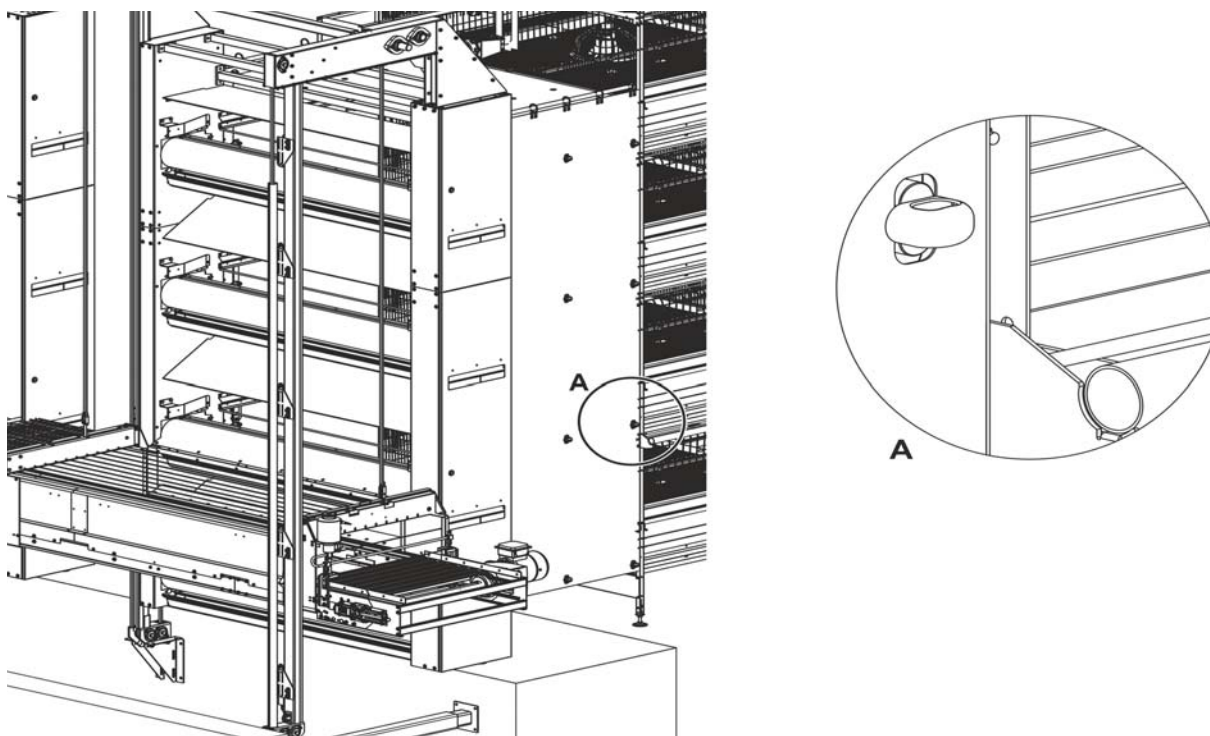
Cortinas de cierre en la zona del conjunto final
